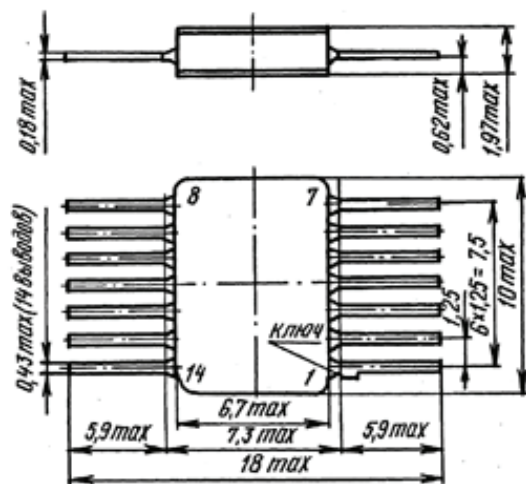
Габаритные чертежи корпусов 401.14-4 и 401.14-5М
